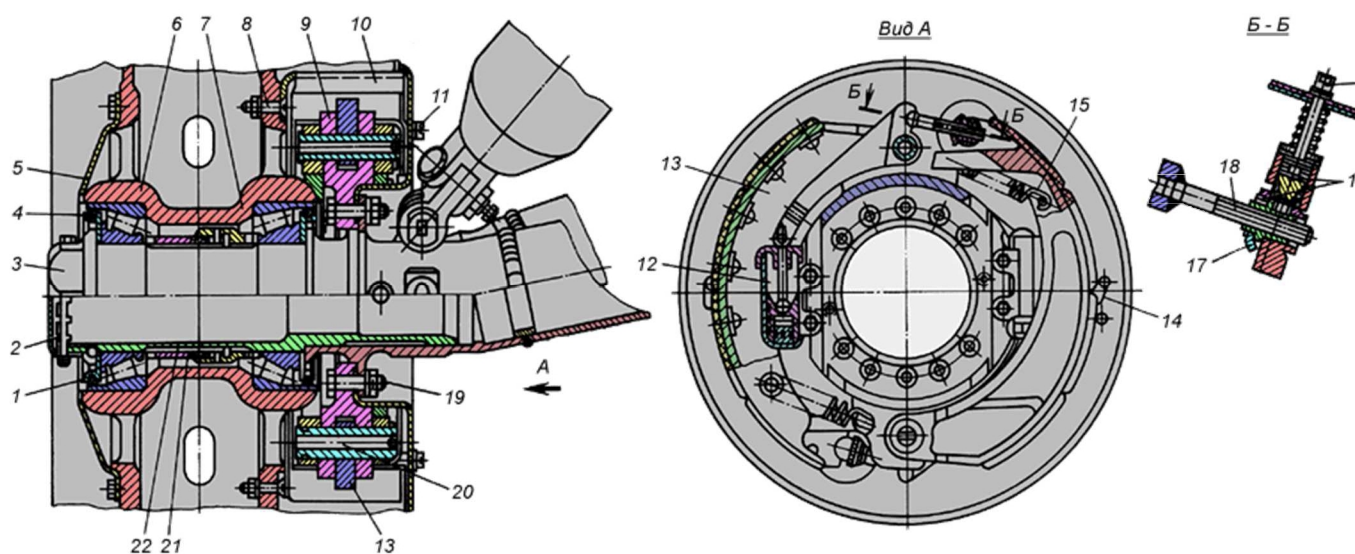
Барабан колеса КТ97 и тормозное устройство
